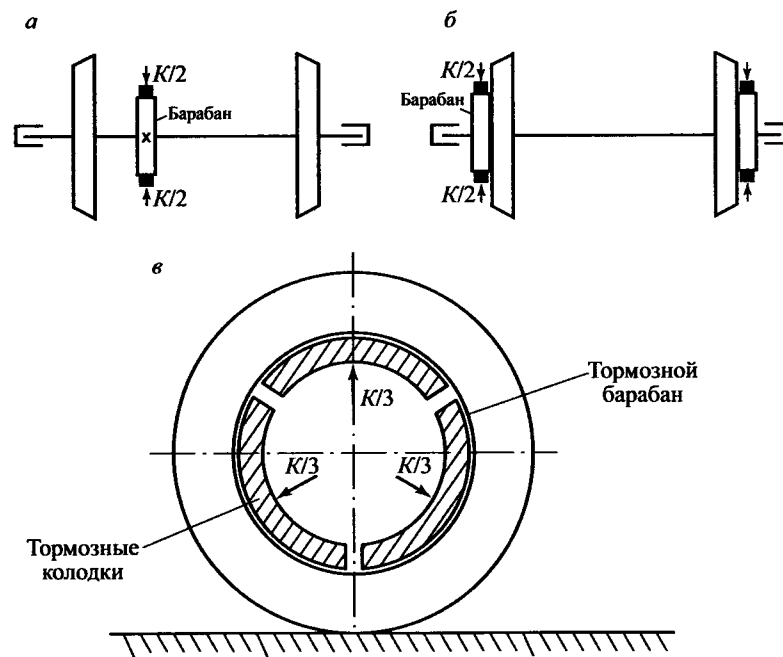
Схемы барабанного тормоза: а — барабан размещен на оси; б — барабан прикреплен к колесному центру; в — внутреннее нажатие тормозных колодок
